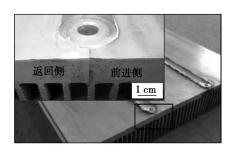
焊缝宏观形貌 Fig. 3 Macrophotograph of welding joint
